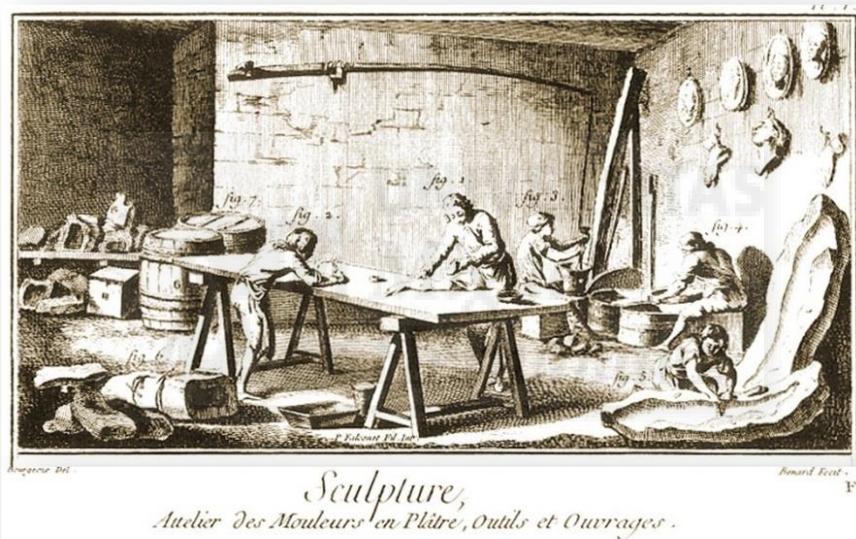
Taller de moldeadores, herramientas y obras: (Fig.1) Moldeador que hace un hueco. (Fig.2) Moldeador que aprieta sobre el hueco. (Fig.3) Obrero machacando yeso. (Fig.4) Obrero tamizando yeso. (Fig. 5) Moldeador barnizando el hueco con aceite caliente. (Fig.6) Hueco del molde listo para colar. (Fig.7) Barriles que sirven para poner el yeso.
